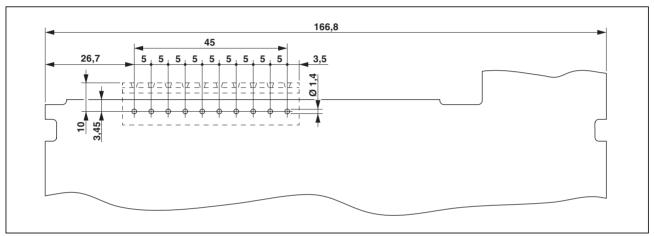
Maßzeichnung der Leiterplatte des Gehäuses bei Verwendung des Anschlusstechnik-Trägers CT10
